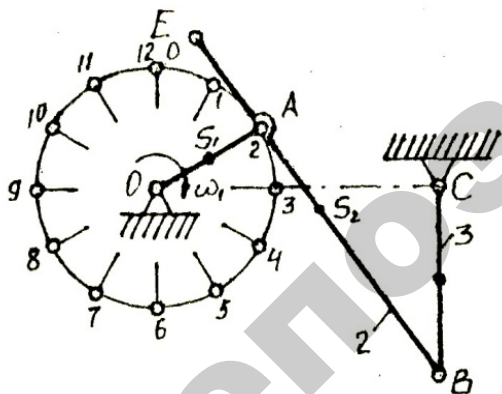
Схема 5 шарнирного четырехзвенника
